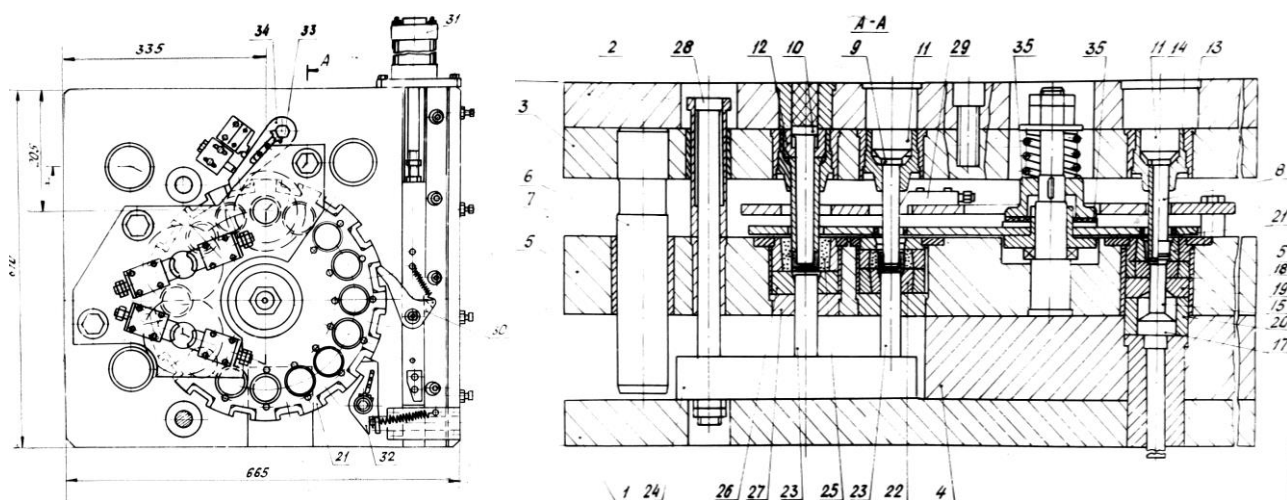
Схема многопозиционного штампа для выдавливания детали типа «стакан»
